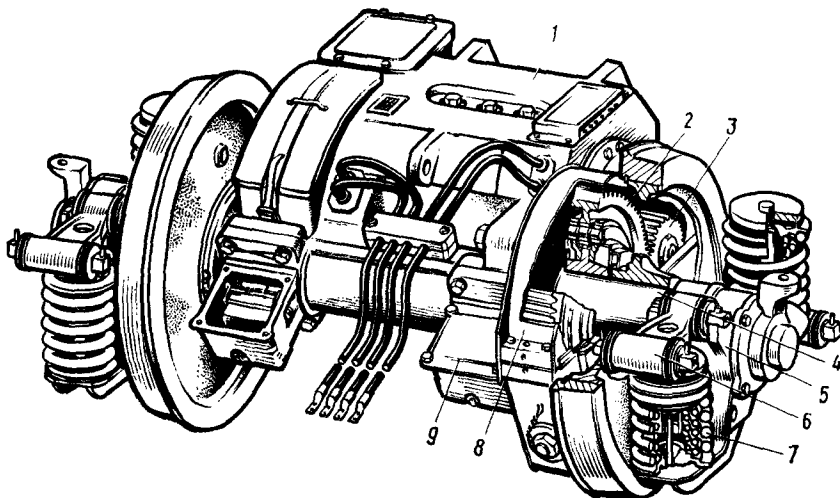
Колесно-моторный блок с опорно-осевым подвешиванием тяговых электродвигателей: 1 — тяговый двигатель; 2 — упругое зубчатое колесо; 3 — шестерня; 4 — колесная пара; 5 — букса; 6 — поводок буксы; 7 — пружины; 8 — кожух редуктора; 9 — моторно-осевые подшипники
